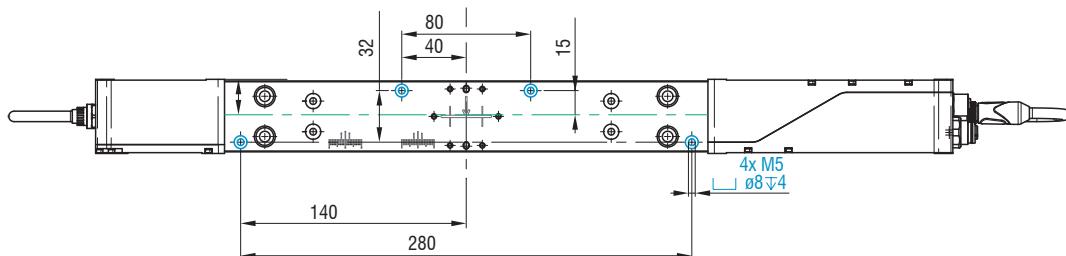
Maßzeichnung Montageschiene ODC2700-10, ODC2700-40, Standardmontage
